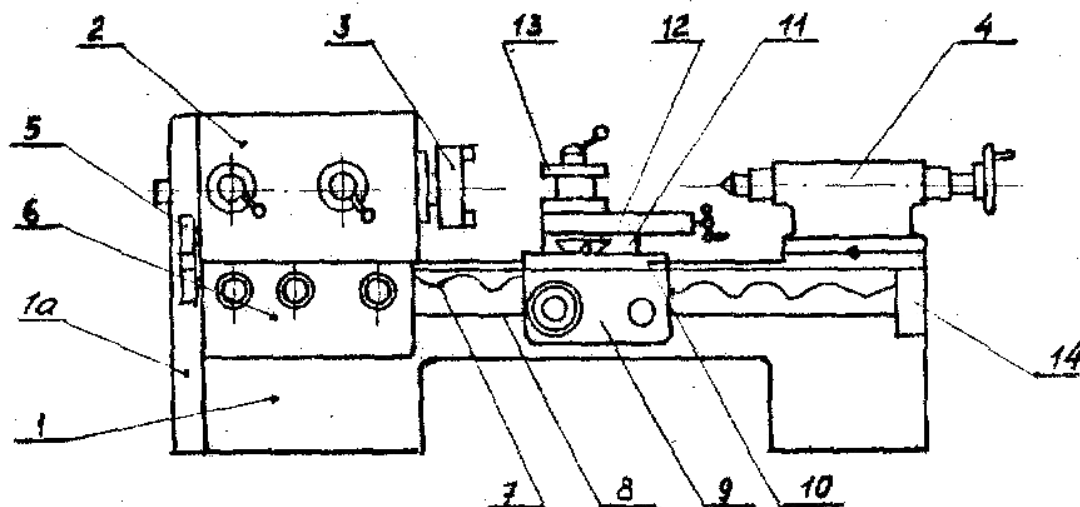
І. Універсальний токарно-гвинторізальний верстат
